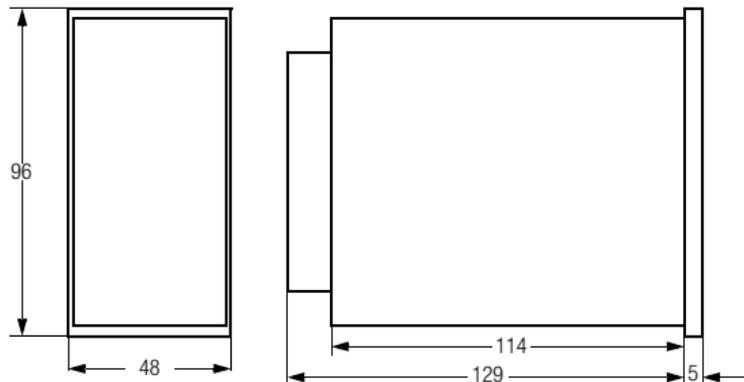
, Gehäuseabmessungen und Schalttafelausschnitt
